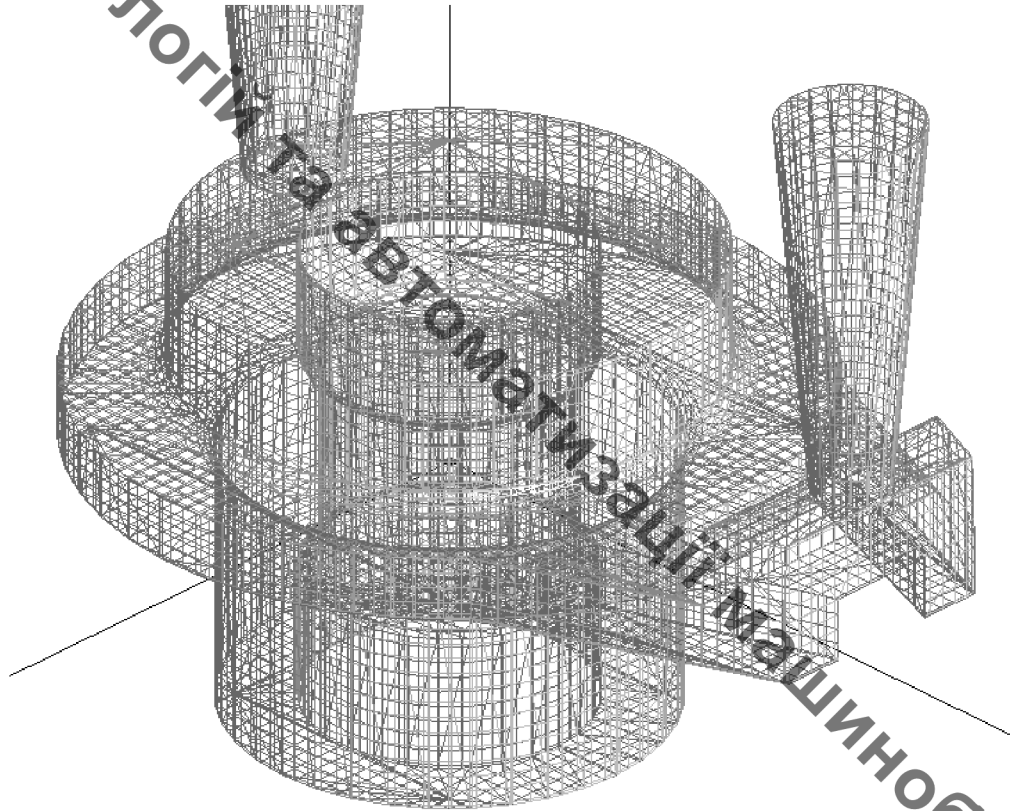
Розрахункова сітка вилівка та ливникової системи
